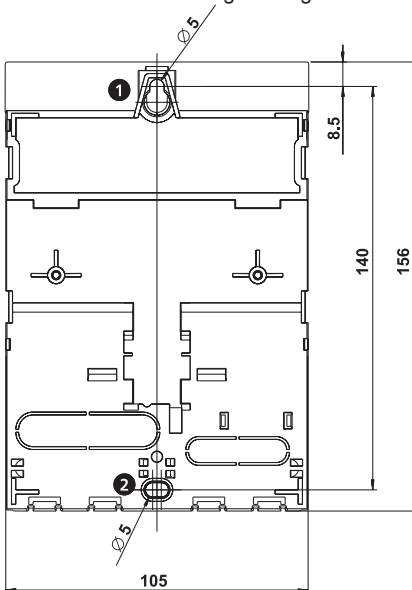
Rückseite des Reglers mit Montageöffnungen oben ❶ und unten ❷
